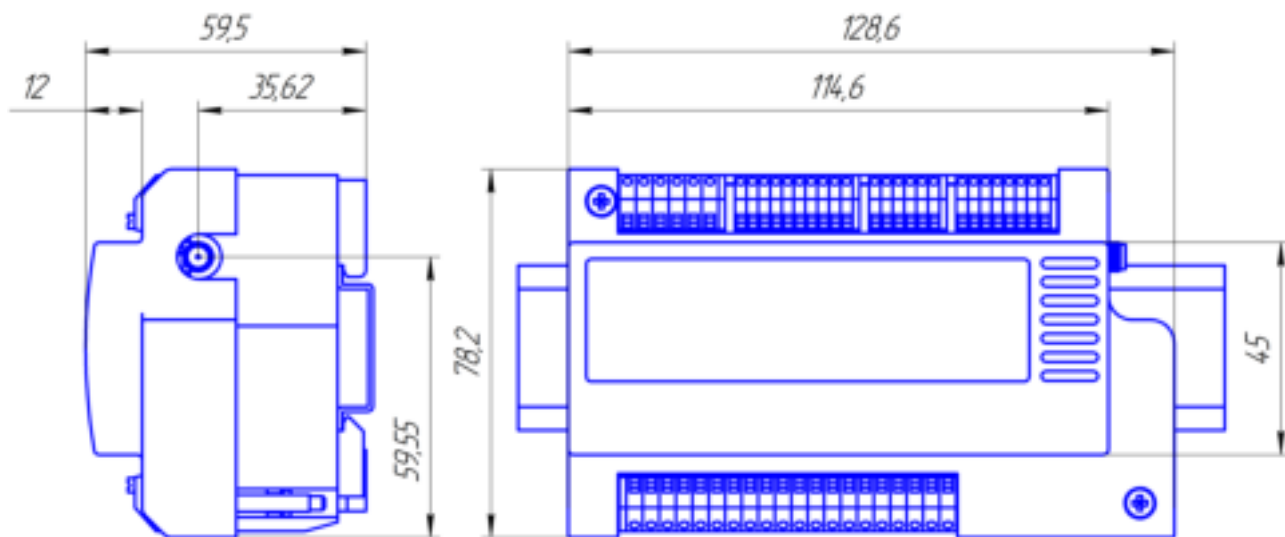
Габаритные и установочные размеры контроллера с креплением на DIN-рейку
